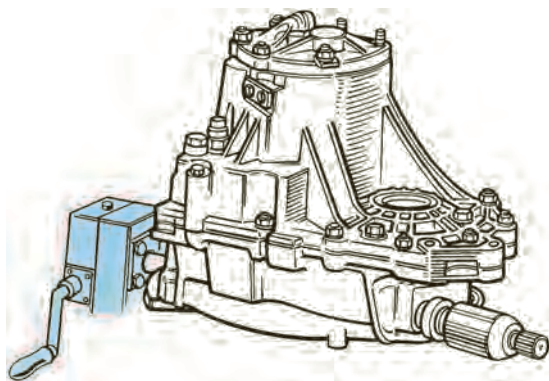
Коробка передач автомобиля ВАЗ-2108, установленная на стенде для разборно-сборочных работ
